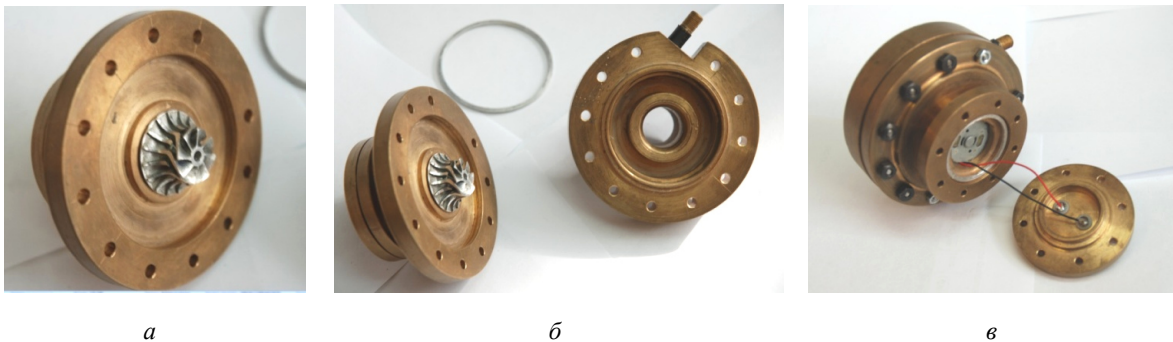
Вид на рабочее колесо со стороны крышки (а); крышка и корпус генератора (б); вид со стороны крышки генератора (в)
